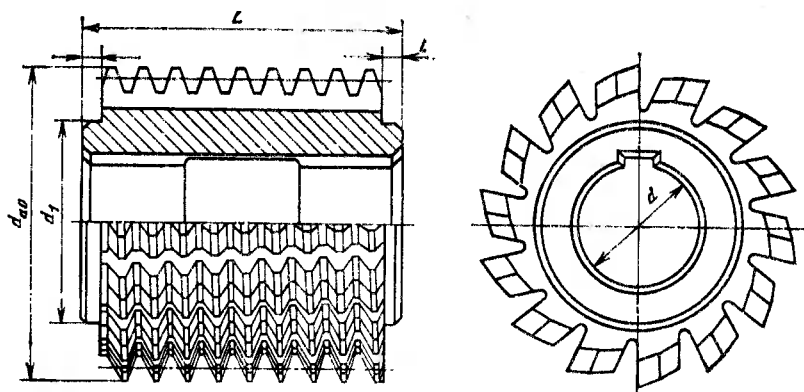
Основные размеры червячной зуборезной фрезы
